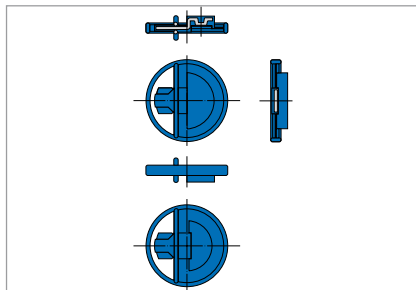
Pièces miniaturisées / Pièces moulées et composites en Simriz®
